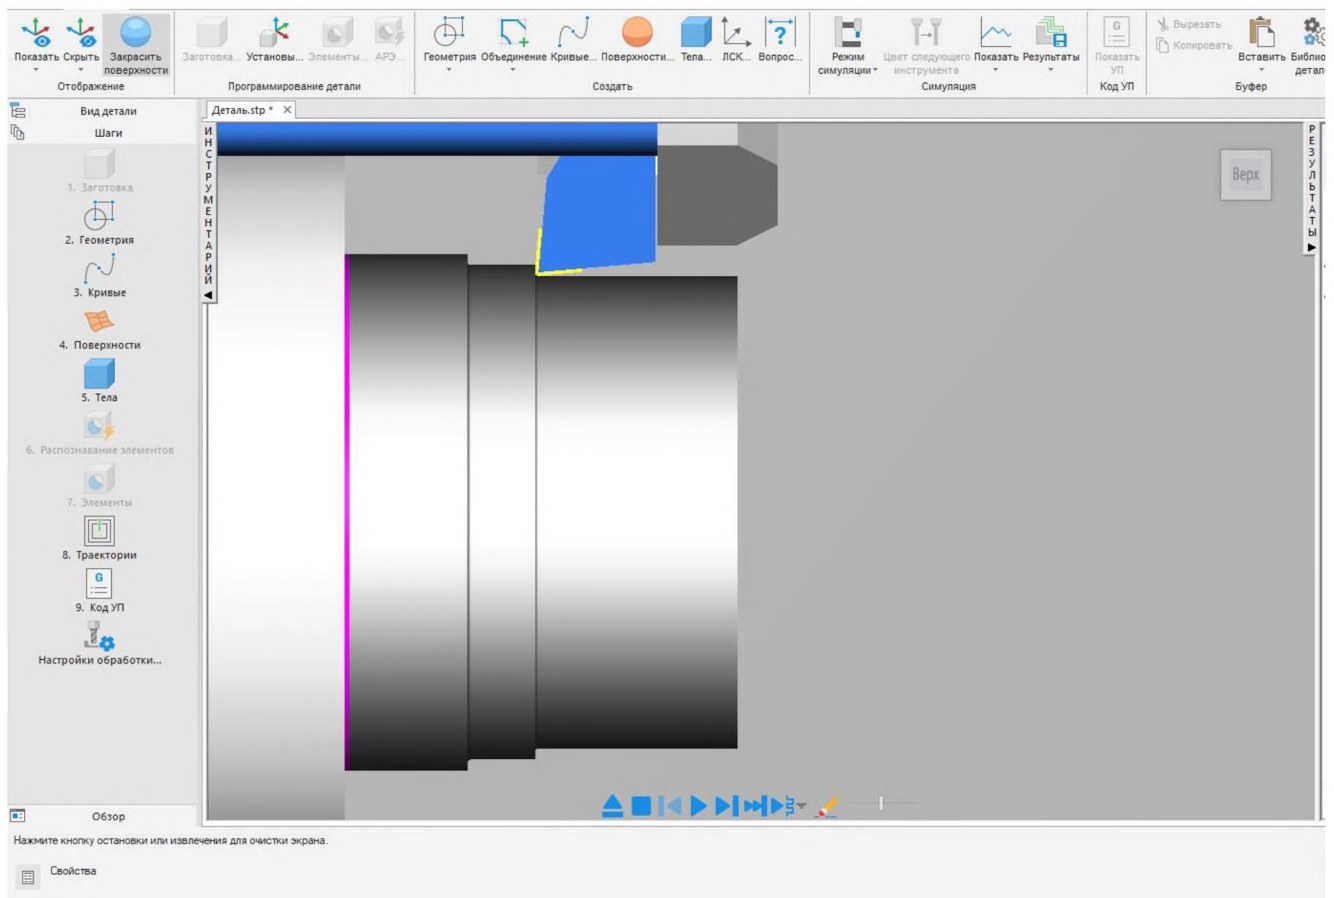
Процесу обробки циліндричної поверхні прохідним різцем
